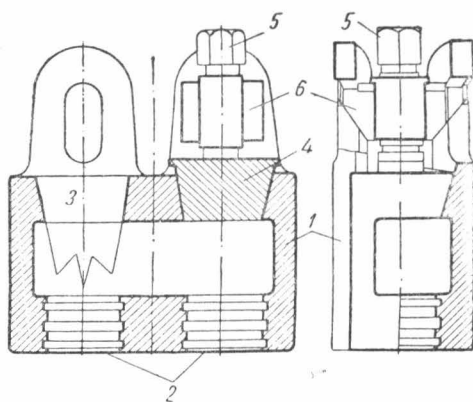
Соединение труб двойниками: 1 — корпус двойника; 2, 3 — отверстия; 4 — пробка; 5 — болт; 6 — распорная гайка.
